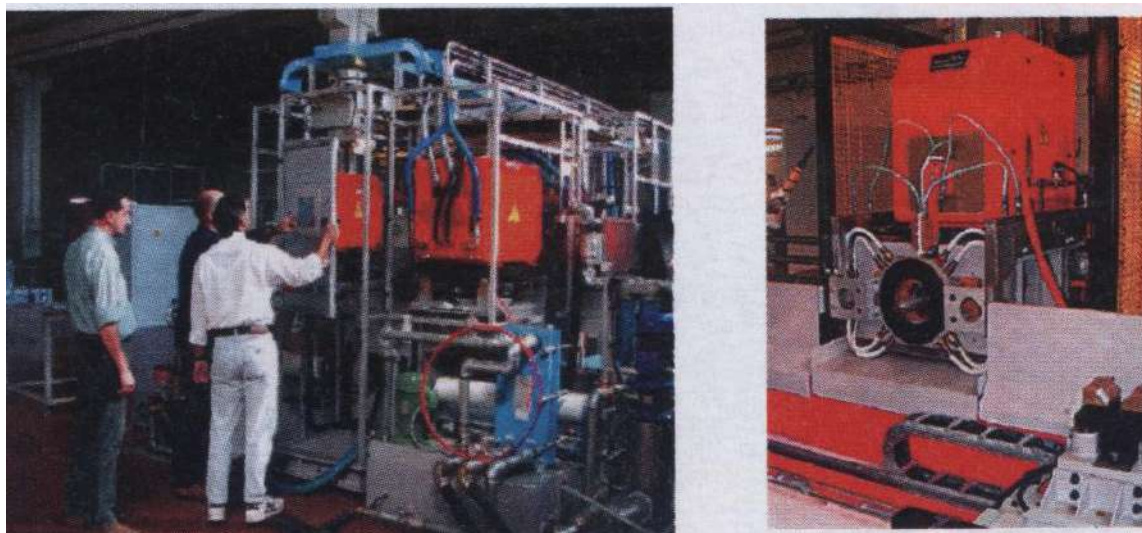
Автоматичний комплекс для гарту професійного інструменту. Частина деталі, індуктор, що термічно оброблюється
